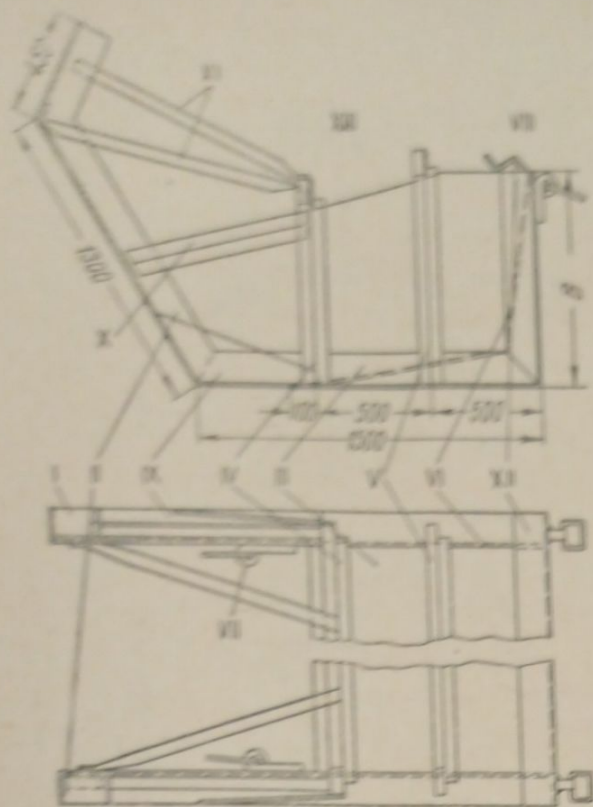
Схема ползункового скрепера упрощенной конструкции (вид сбоку и вид сверху).
